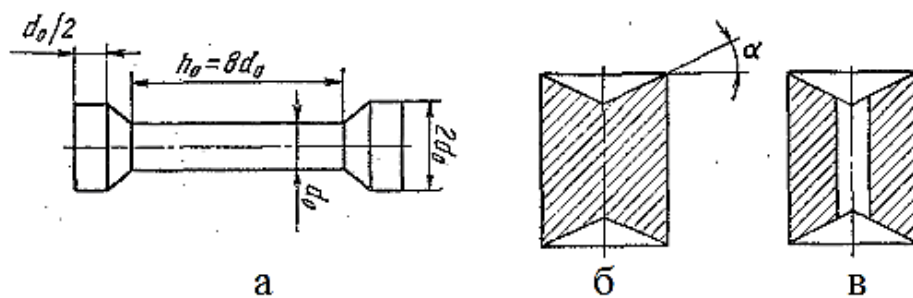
Можливі форми зразків для випробування на стиск [4]: а) циліндричний подовжений зразок з головками для прецизійних вимірювань, б) стандартний зразок, в) зразок з видаленою серцевиною для випробувань крихких матеріалів
